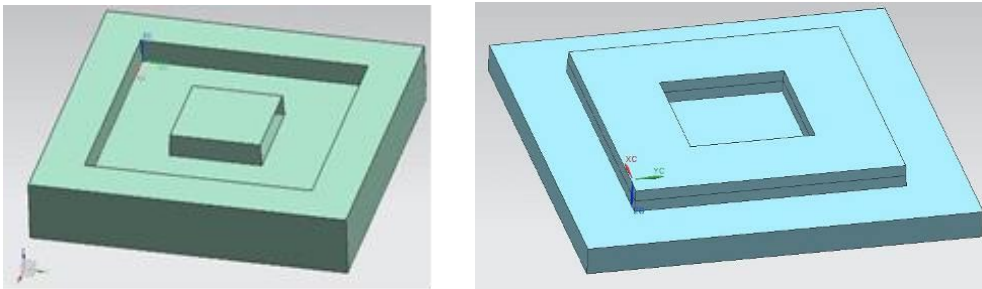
Molde hembra (izquierda) y molde macho (derecha).
